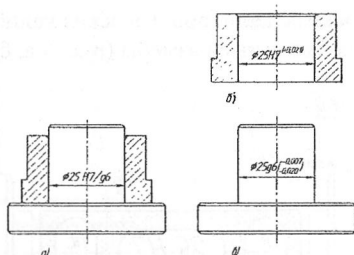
Эскизы гладкого цилиндрического соединения (а) и его деталей (б,в).
